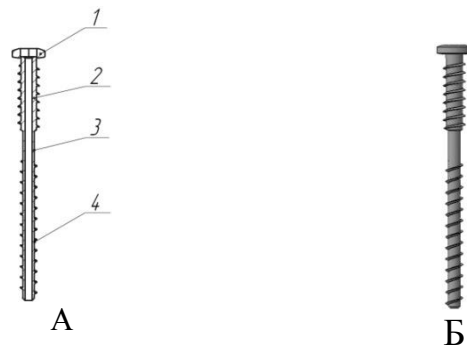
Схематичне зображення зустрічно-компресуючого гвинта: А - креслення гвинта (1 - головка гвинта; 2 - різьба діаметром 4,5 мм; 3 - тіло гвинта; 4 - різьба діаметром 3,5 мм.), Б - загальний вигляд гвинта (3D - модель).
